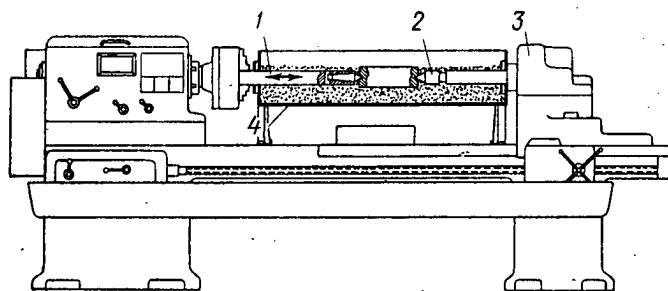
Схема установки сварочного аппарата АДС-1000 на станке.
